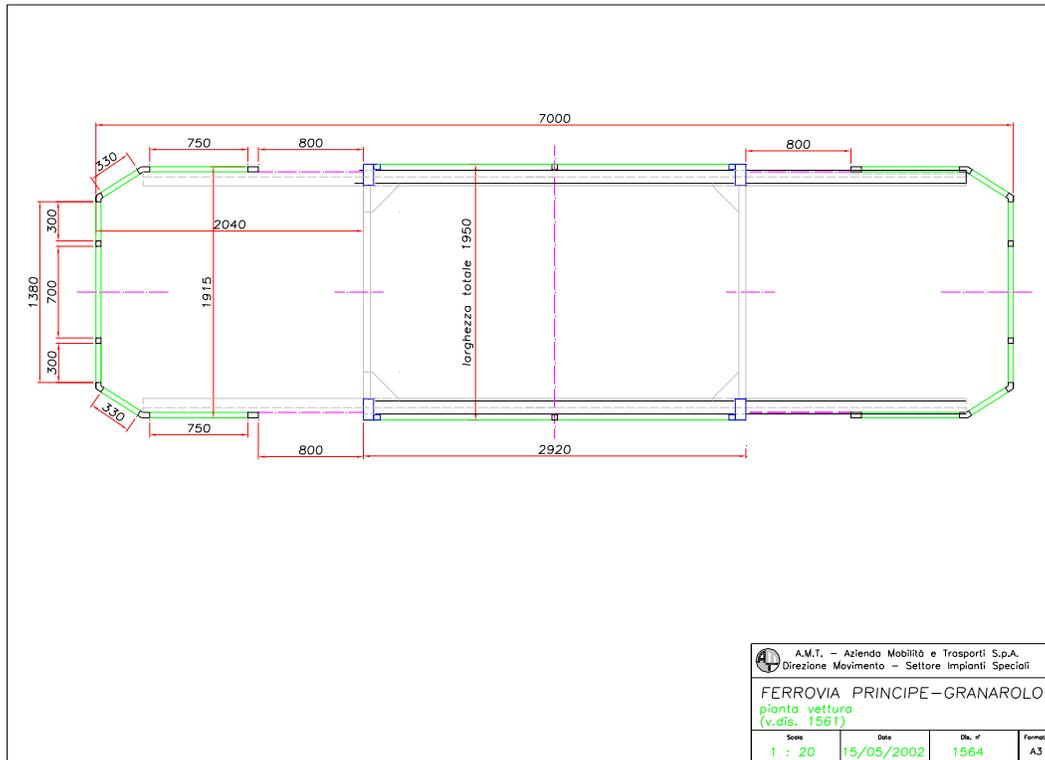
Struttura metallica, pianta- disegno AMT 1564
